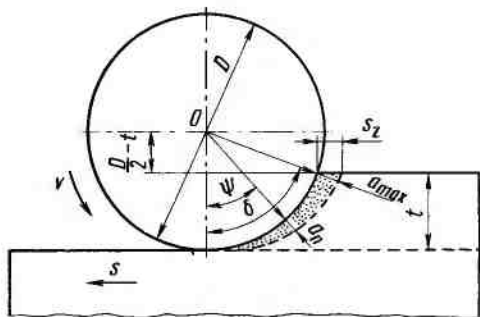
Элементы резания при работе цилиндрической фрезой
